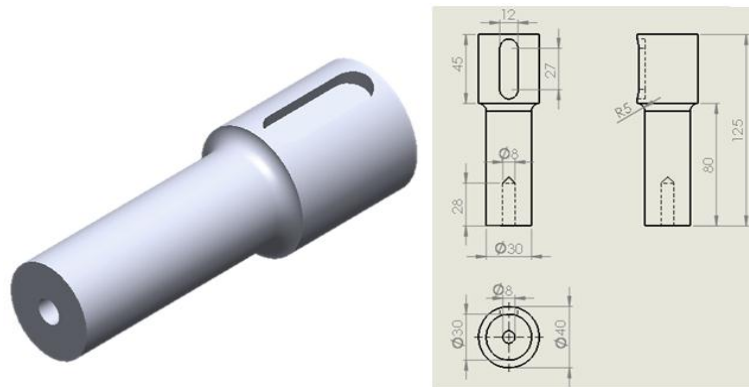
Izquierda) Eje donde se va a ubicar el disco de corte. Derecha) Dimensiones del eje de corte en mm.
